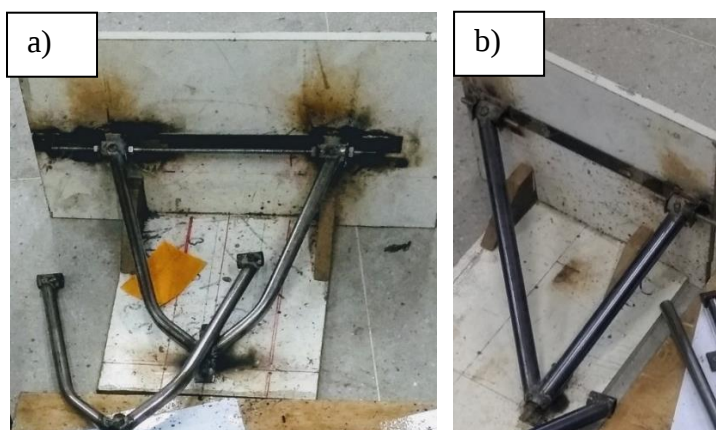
Gabarito regulável para auxiliar a soldagem.
